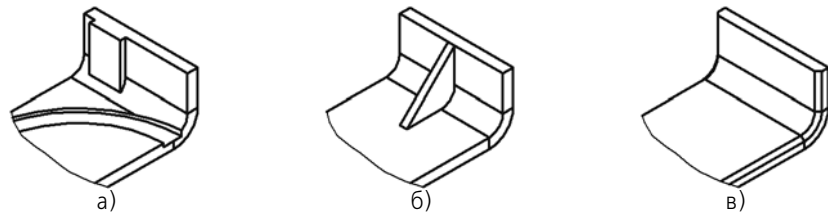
Примеры формообразующих и конструктивных элементов, делающих невозможным разгибание сгиба:
